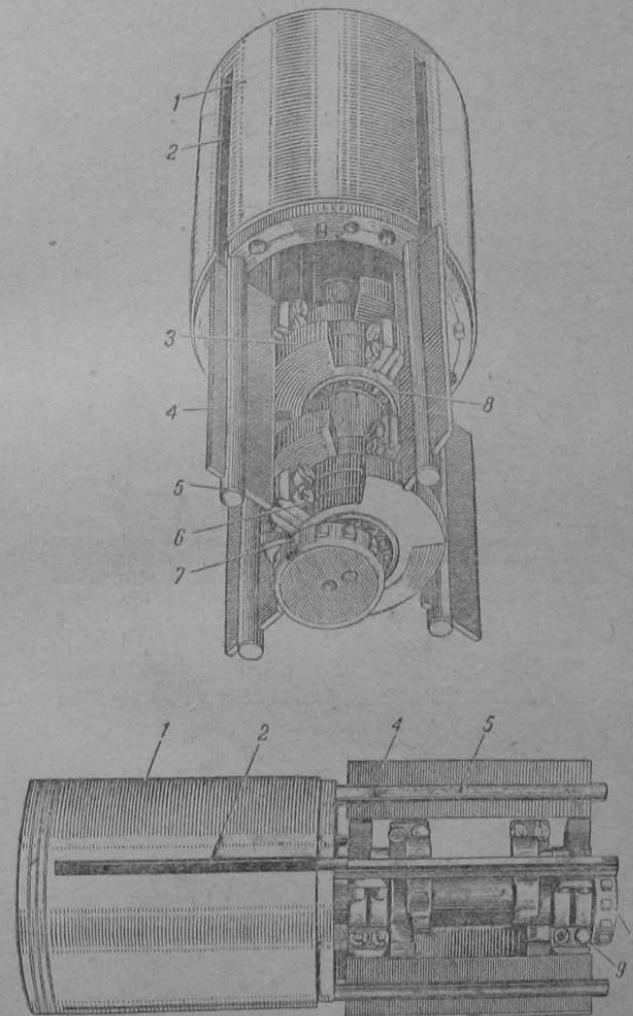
Ротор нагнетателя двигателя С2Б с внутренними деталями:
